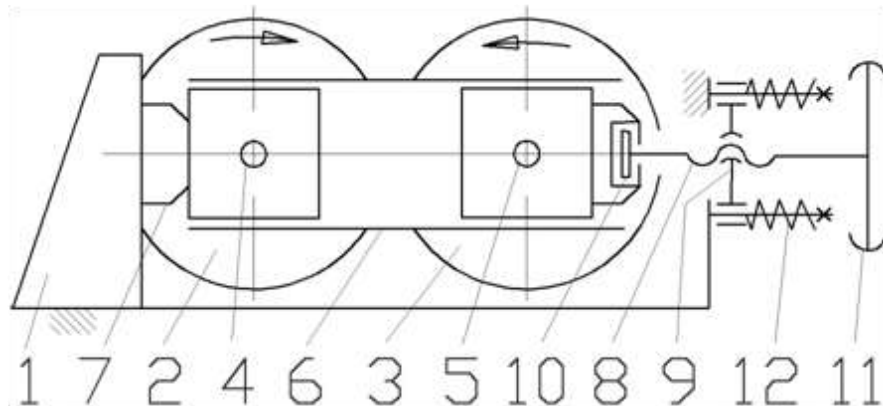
Схема установочного механізму плющильного верстата.
